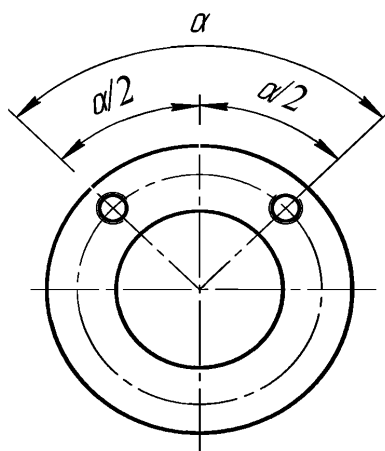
Расположение отверстий для типов присоединений F03–F60
